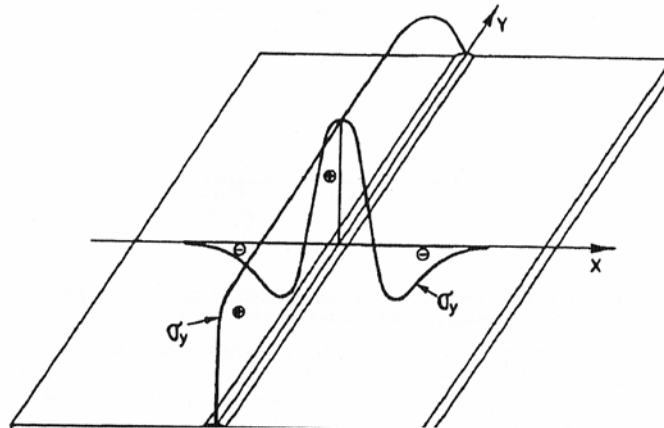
Comportamento de tensões na direção de soldagem (ANTUNES, 1995)
